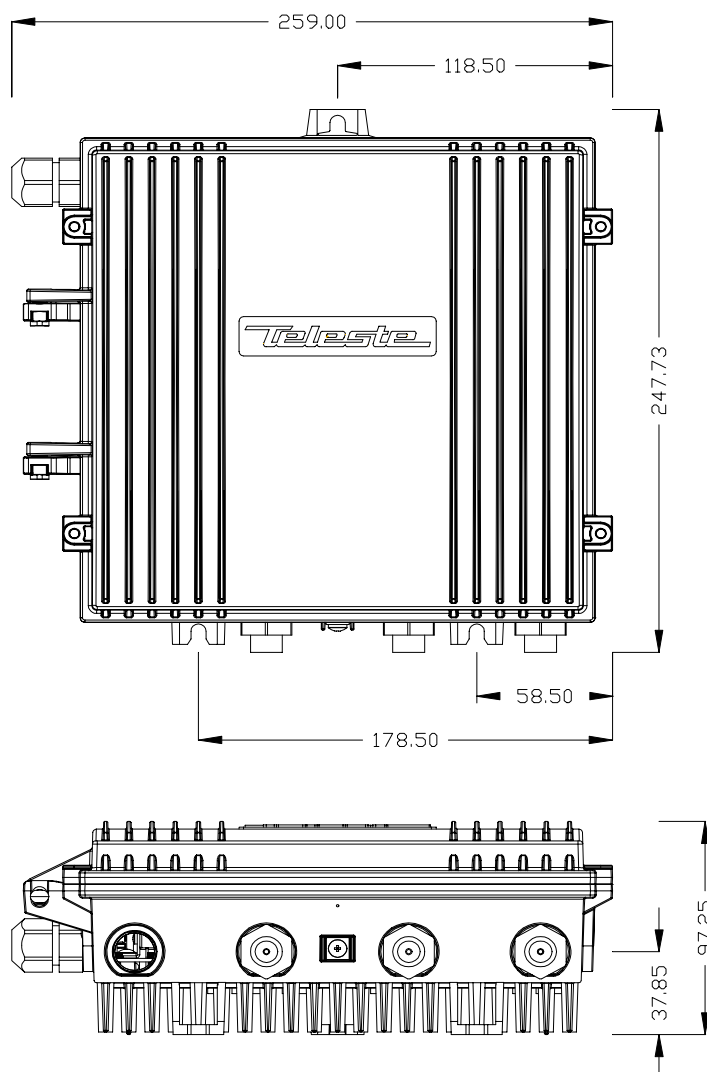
Размеры корпуса AC800 –виды сверху и сбоку
